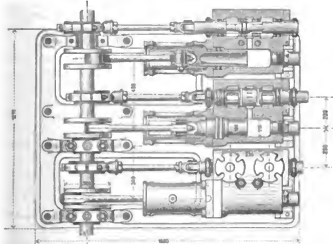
bis 223. Druckwassermaschine von 26 Pferdekraften Nutzleistung.
